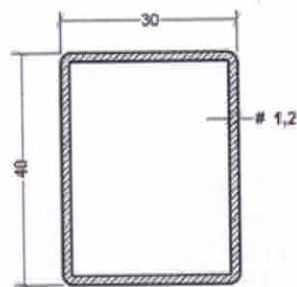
A –Tubo de perfil retangular, opção de uso em substituição ao perfil oblongo (Figura 8) (medidas em milímetros)
